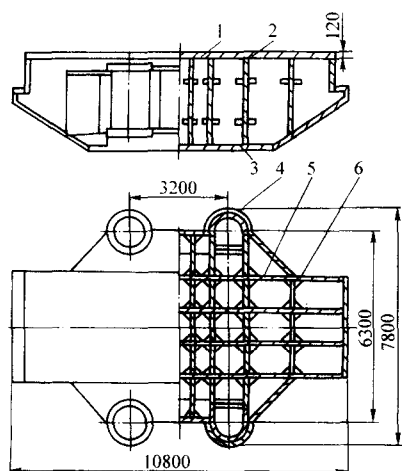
重型压机下横梁电渣焊接结构
